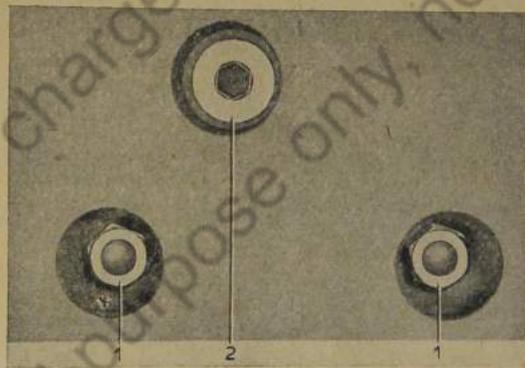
Sechskantmuttern für Hinterradantriebsgehäuse am 6. Querträger abschrauben
